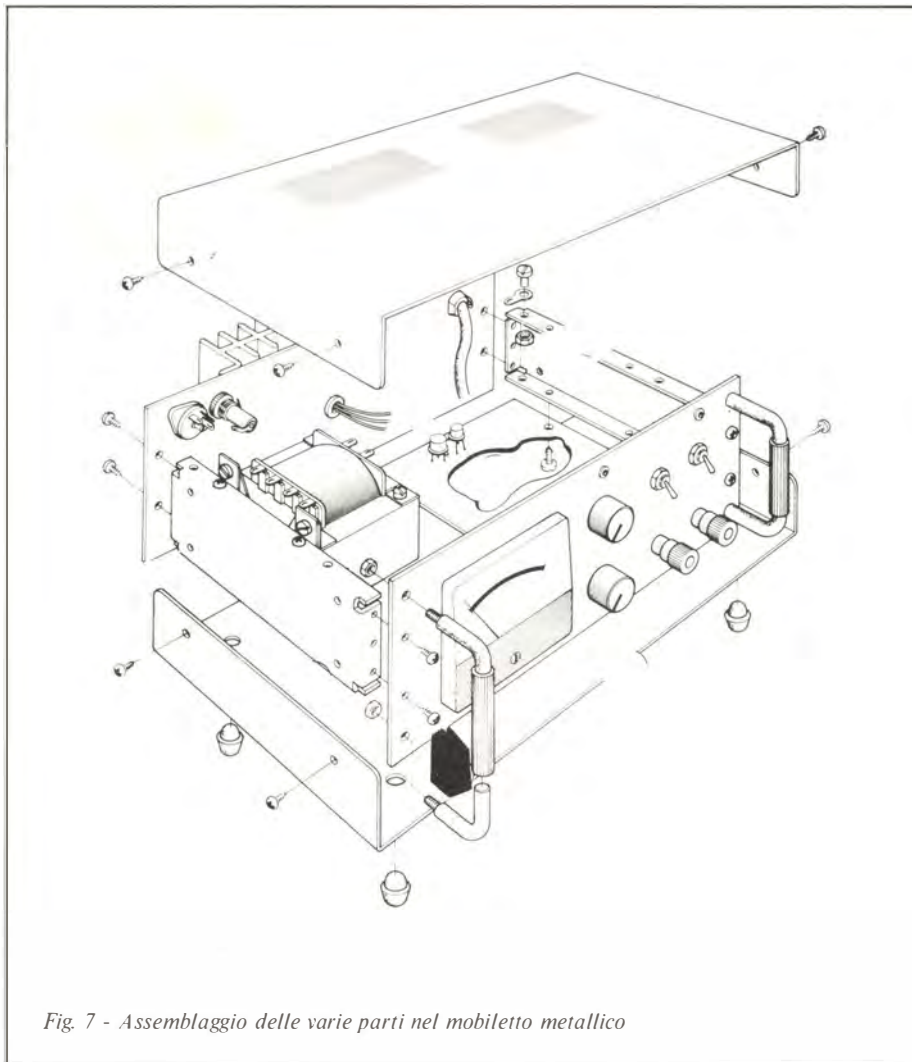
Assemblaggio delle varie parti nel mobiletto metallico
